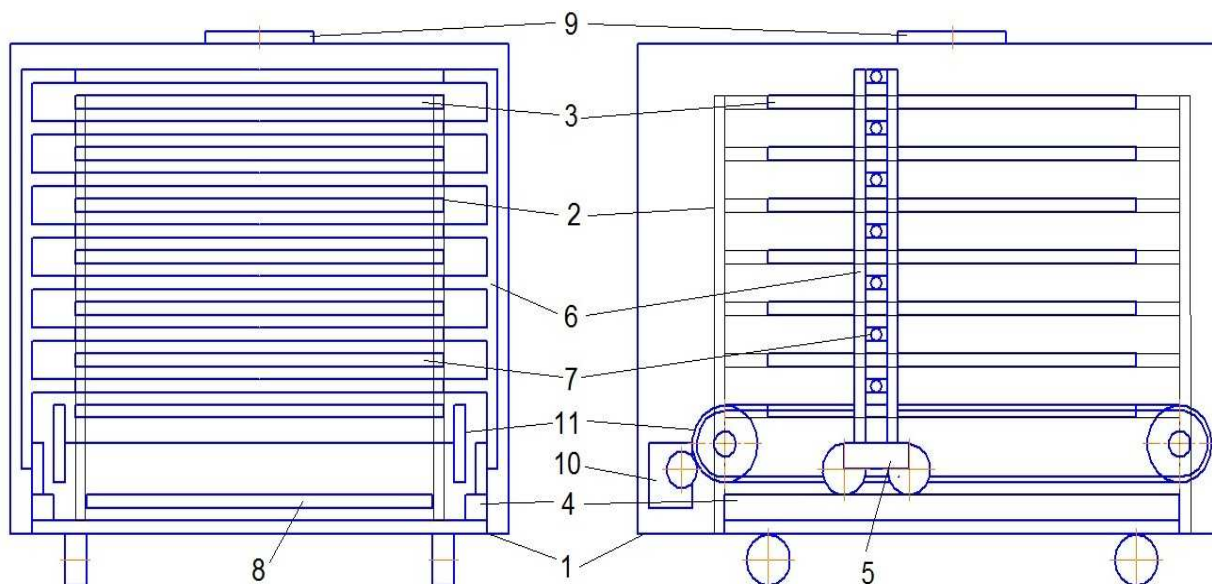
Схема камеры динамической инфракрасной сушки
